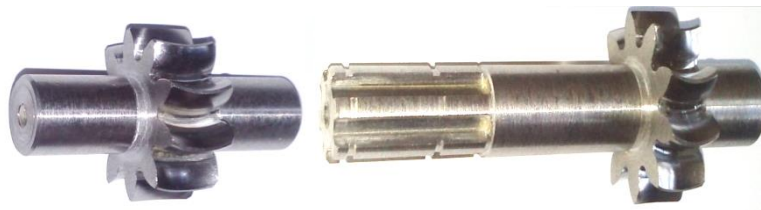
Розроблена пара зубчастих коліс з арочним зубом.
